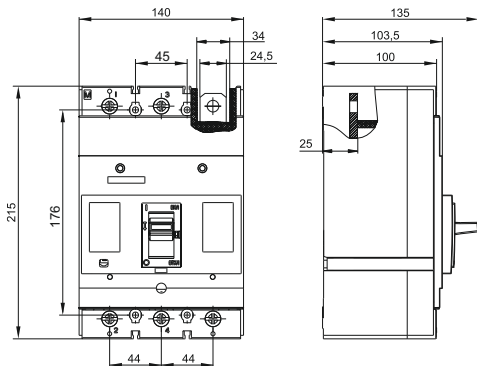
Габаритные и установочные размеры выключателя ВА44-39 / Figure 9 — Overall and installation dimensions of the switch VA44-39 / 9-сурет — ВА44-39 ажыратқышының габариттік және орнатқыш өлшемдері / Figura 9 — Dimensiunile generale și de montare ale întreruptorului VA44-39
